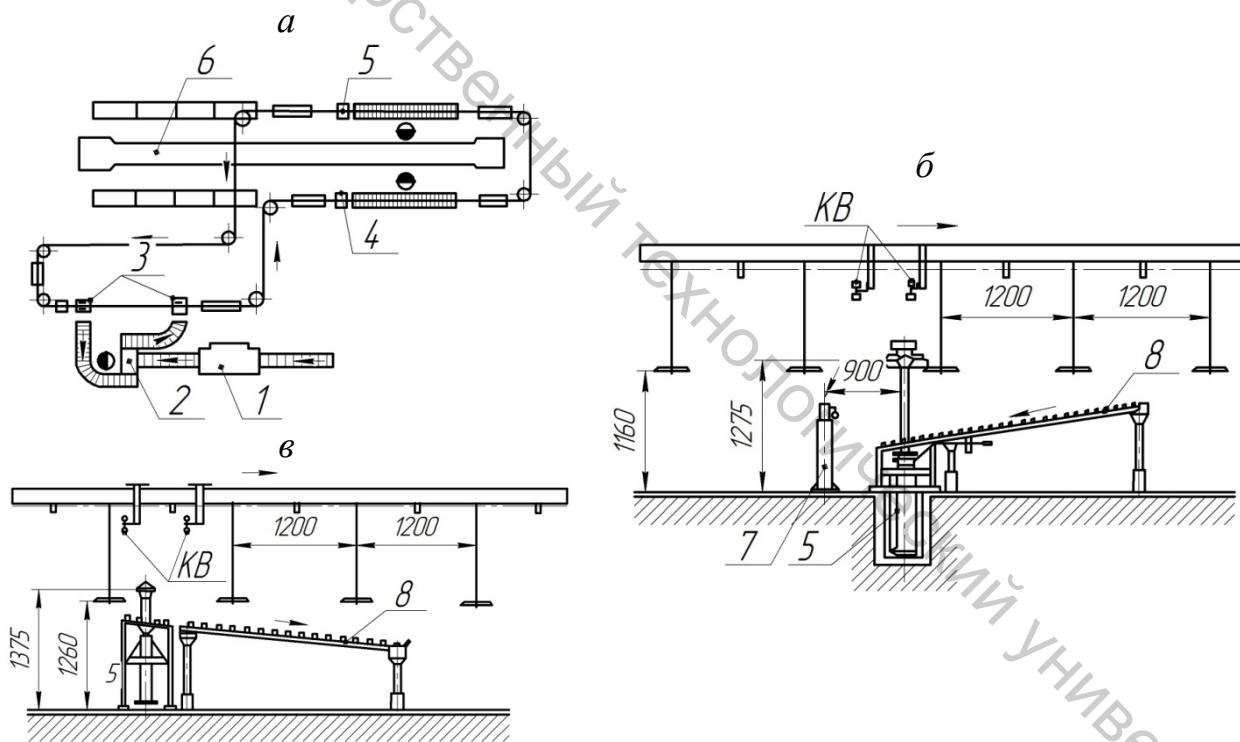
Схема планировки сборочного участка с подвесным конвейером при автоматической навеске и съёмке тяжёлых деталей с конвейера: а – схема планировки участка; б – схема навески на подвесной конвейер; в – схема съёма деталей с подвесного конвейера; 1 – моечная машина; 2 – пункт контроля; 3 – пункты навешивания деталей на конвейер; 4 – пункты съёма; 5 – пневмоподъёмник; 6 – сборочный конвейер; 7 – предупредитель; 8 – роликовый конвейер
